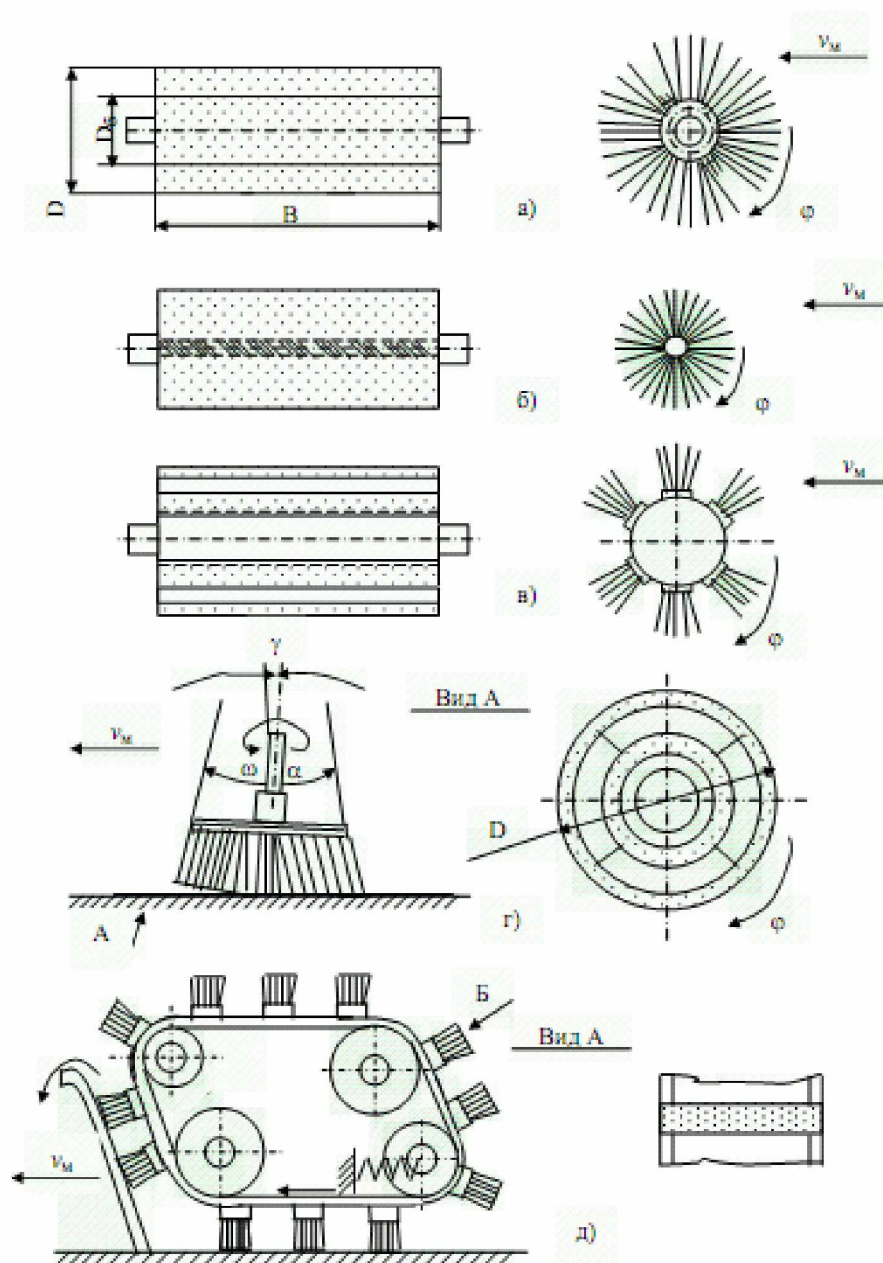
Конструкции подметальных щеток: а – цилиндрическая щетка с креплением ворса на перфорированных бандажах; б – цилиндрическая щетка с креплением ворса навивкой троса на сердечник; в – цилиндрическая щетка с плоскими секциями ворса; г – коническая лотковая щетка с концентрическими рядами ворса; д – ленточная щетка с плоскими секциями ворса
